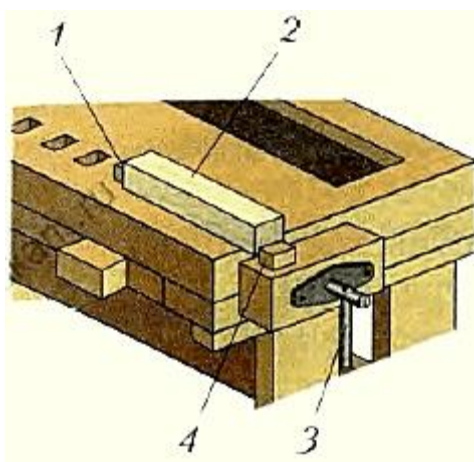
Закрепление заготовки на верстаке: 1 — клин стола; 2 — заготовка; 3 — рукоятка зажима; 4 — клин заднего зажима
